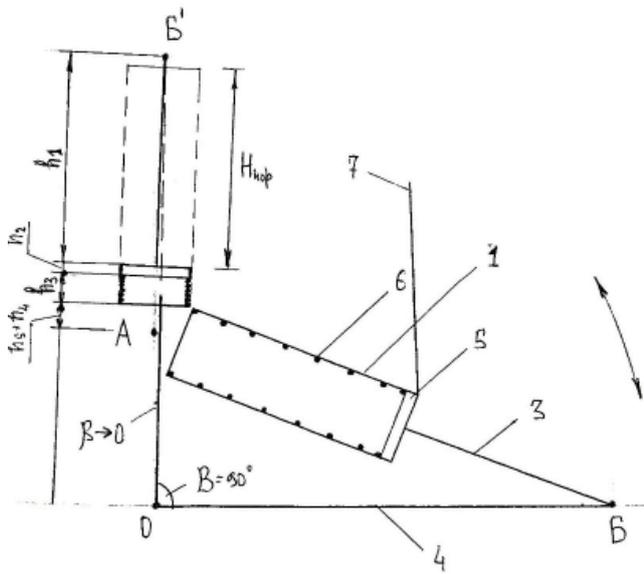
Обозначение геометрических размеров гидроцилиндра и подножки устройства
